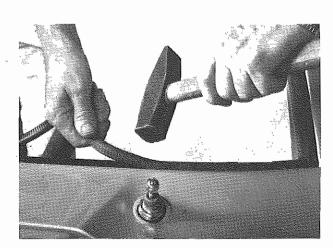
Montare guarnizione "Guistall" Assemble "Guistall" gasket
